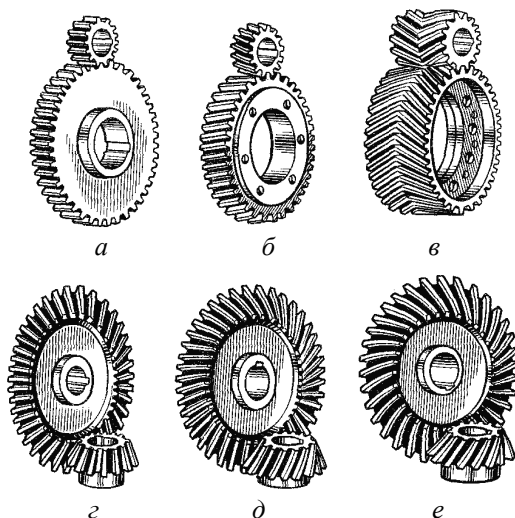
Зубчатые колеса цилиндрические и конические
